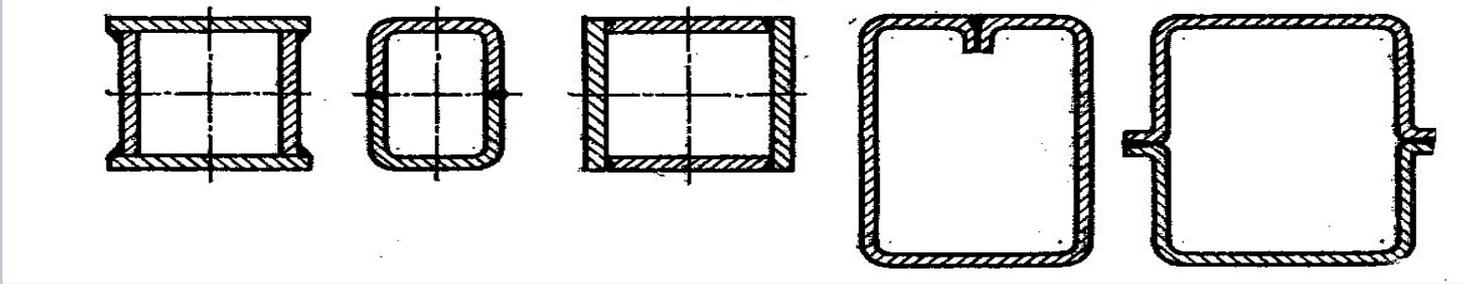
Типы поперечных сечений сварных коробчатых балок
